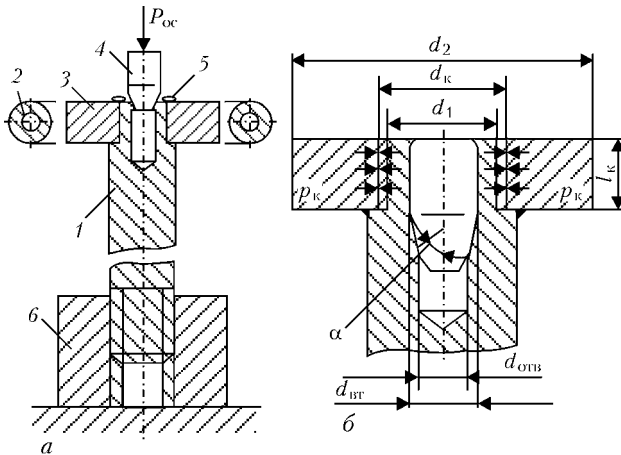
Схема моделирования процесса (а) сваркопайки на образцах (б): 1 – шпилька; 2 – индуктор; 3 – шайба; 4 – цилиндрическая вставка; 5 – активирующее вещество; 6 – упор
